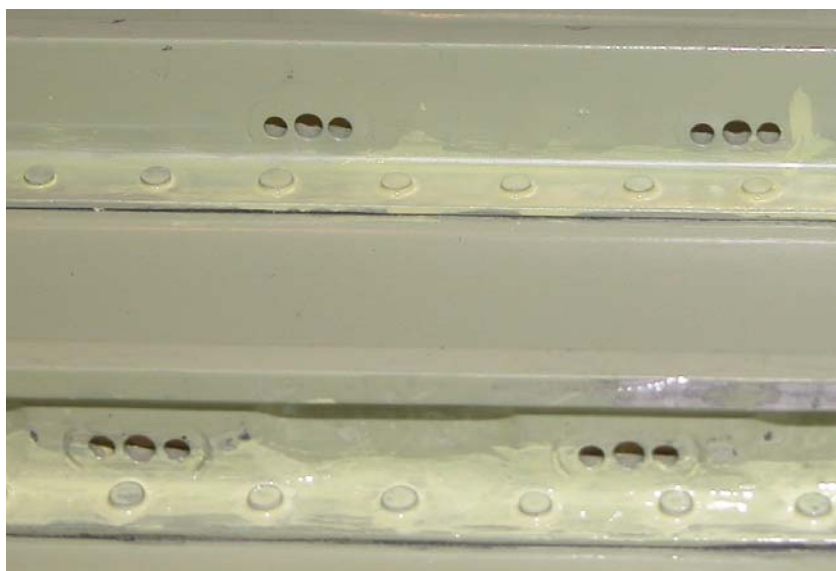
Фрагмент растянутой панели крыла с отверстиями для перетекания топлива
